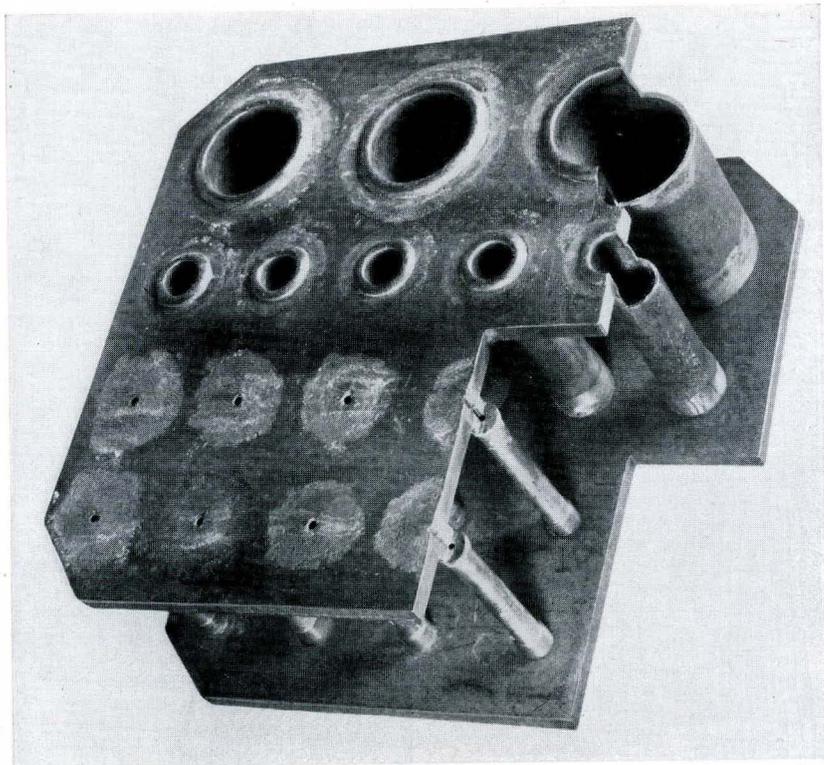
Mit der Schlauchelektrode durch Lichtbogenschweißung in die kupferne Feuerbüchse wand eingeschweißte Stehbolzen. Das Verfahren ist versuchsweise auch bei Heiz- und Rauchrohren angewendet worden. Die Schweißung erfolgte in senkrechter Lage.
